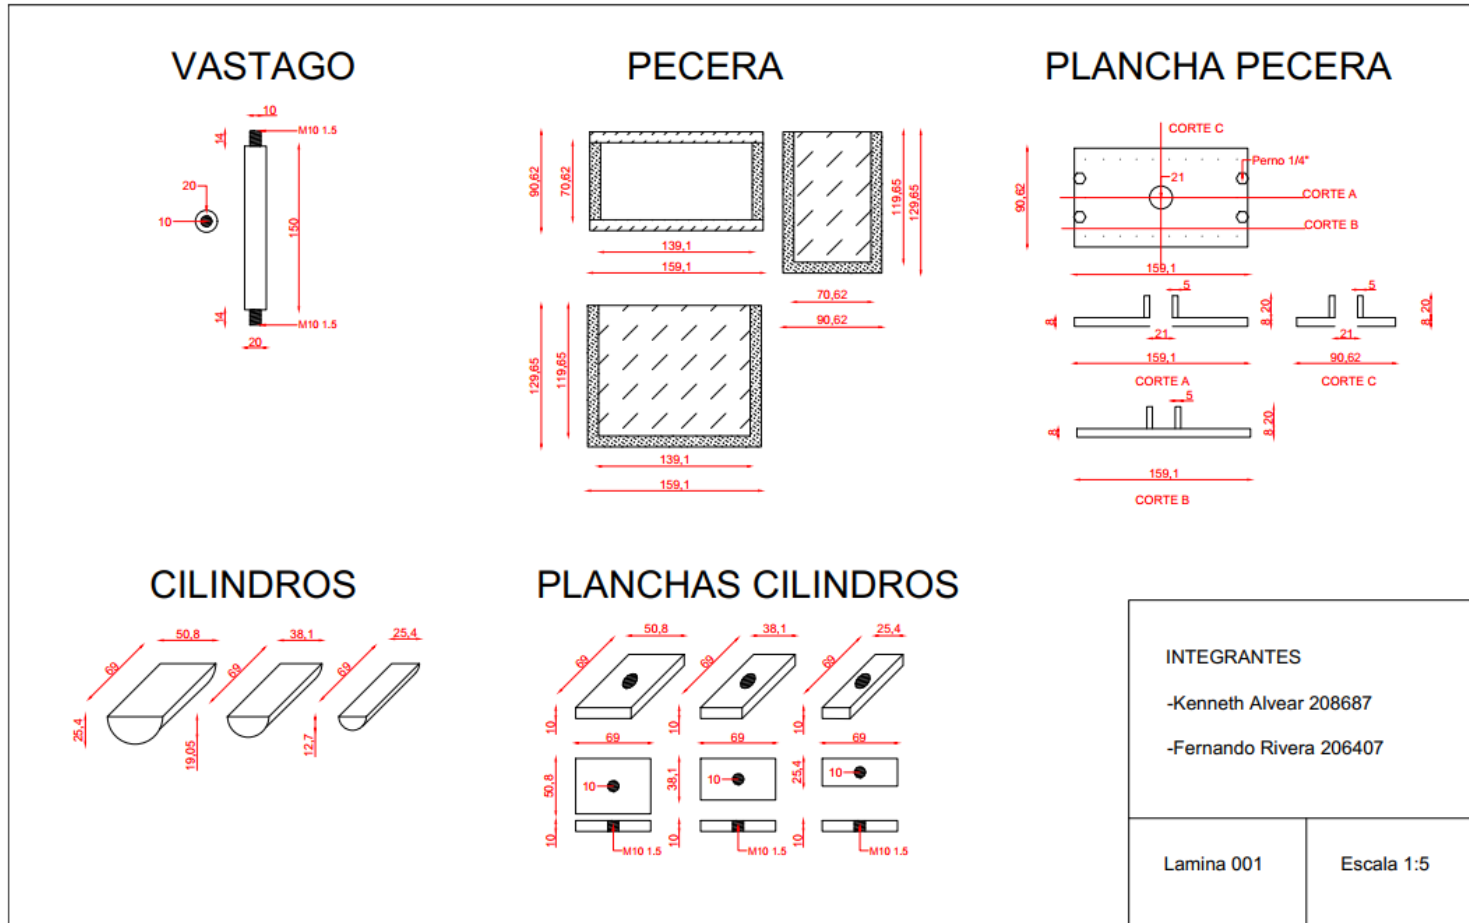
Plano Piezas de Ensamblaje (No a escala)
